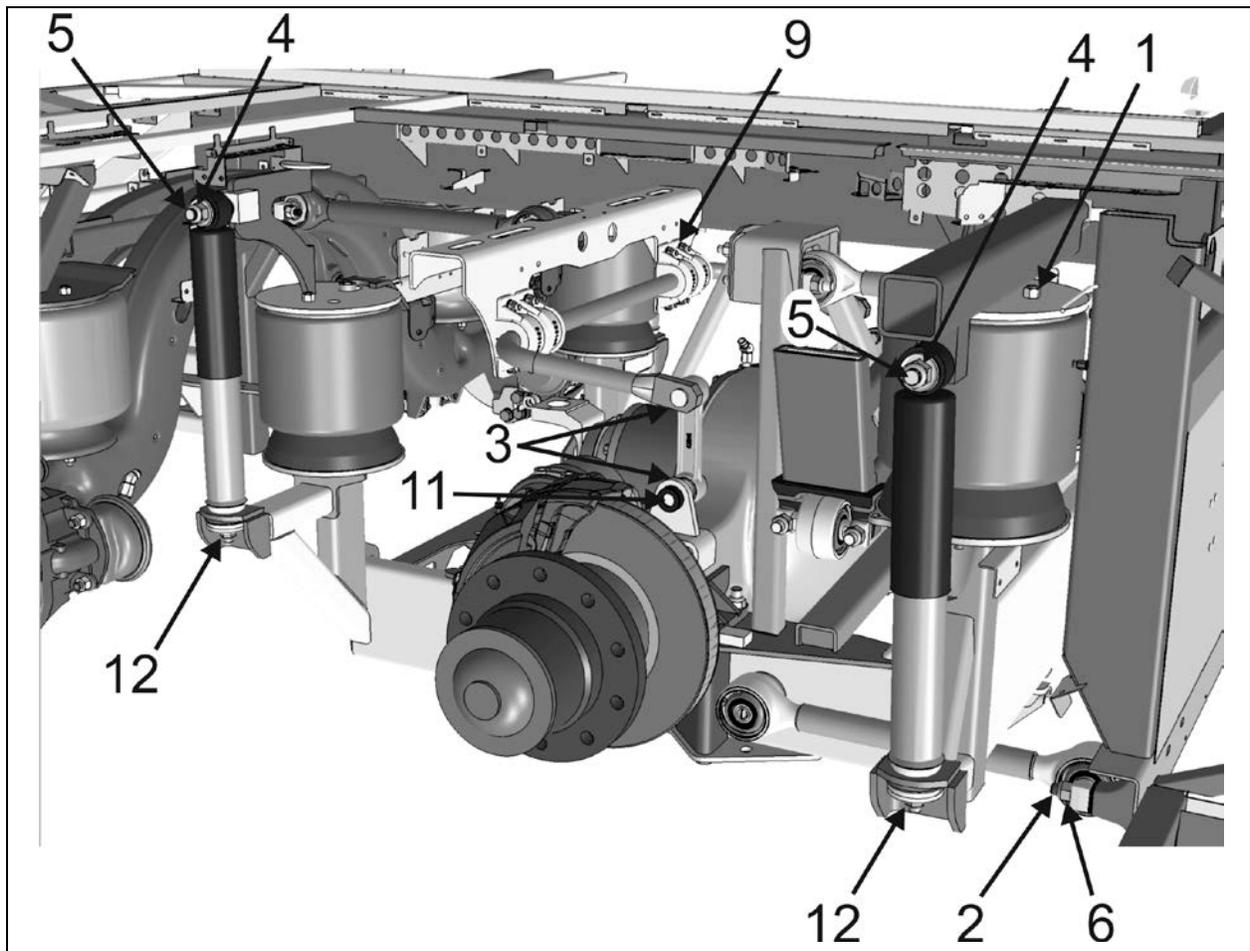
COUPLES DE SERRAGE – ESSIEU MOTEUR
